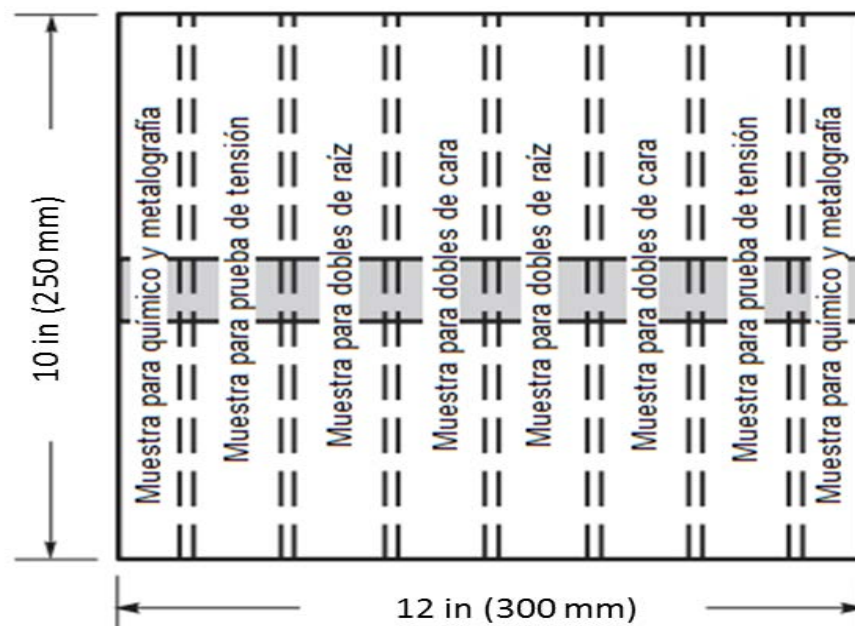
Esquema de la segmentación de los cupones de soldadura.
